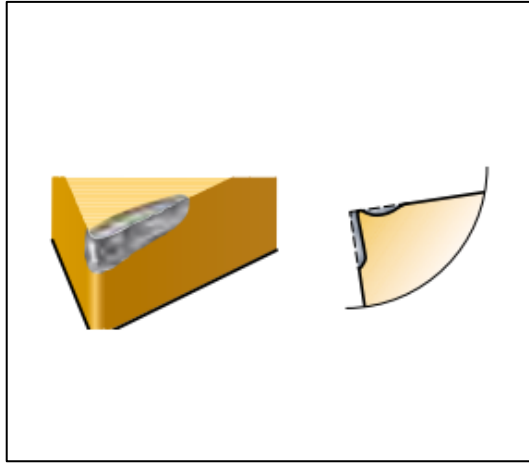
Representação de desgaste de flanco em aresta de corte (17).
